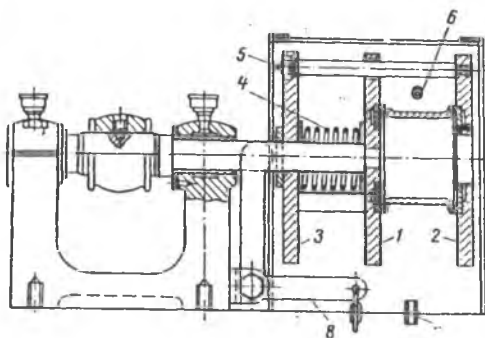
Приспособление для центробежной заливки подшипника.
